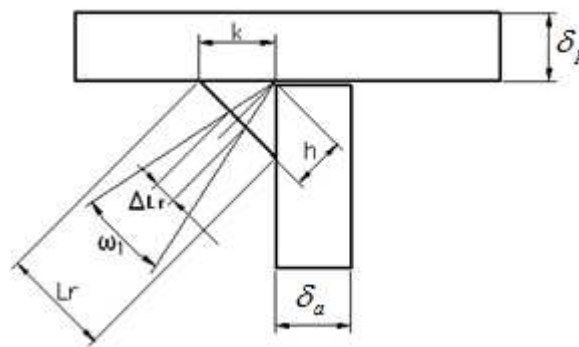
Geometría de la contracción del cordón de soldadura
